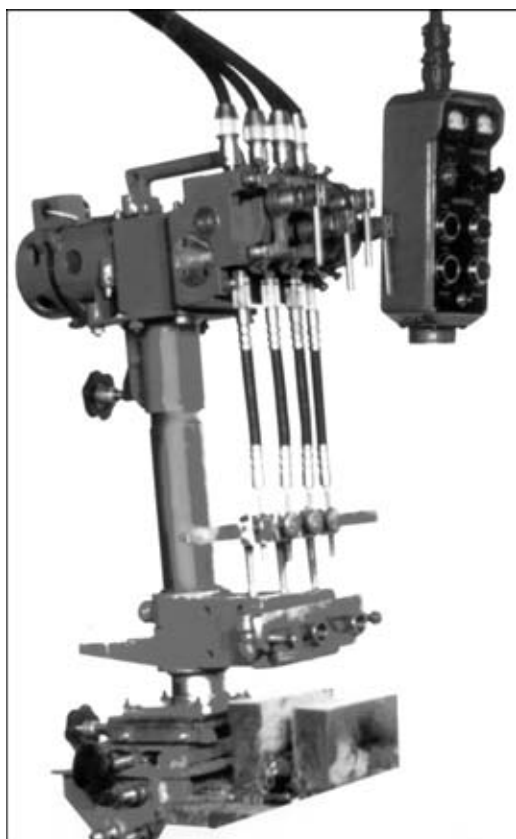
Автомат для электрошлаковой сварки А 1304
